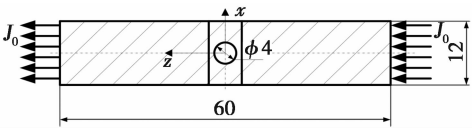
含球形孔洞缺陷的焊接接头 (mm)
